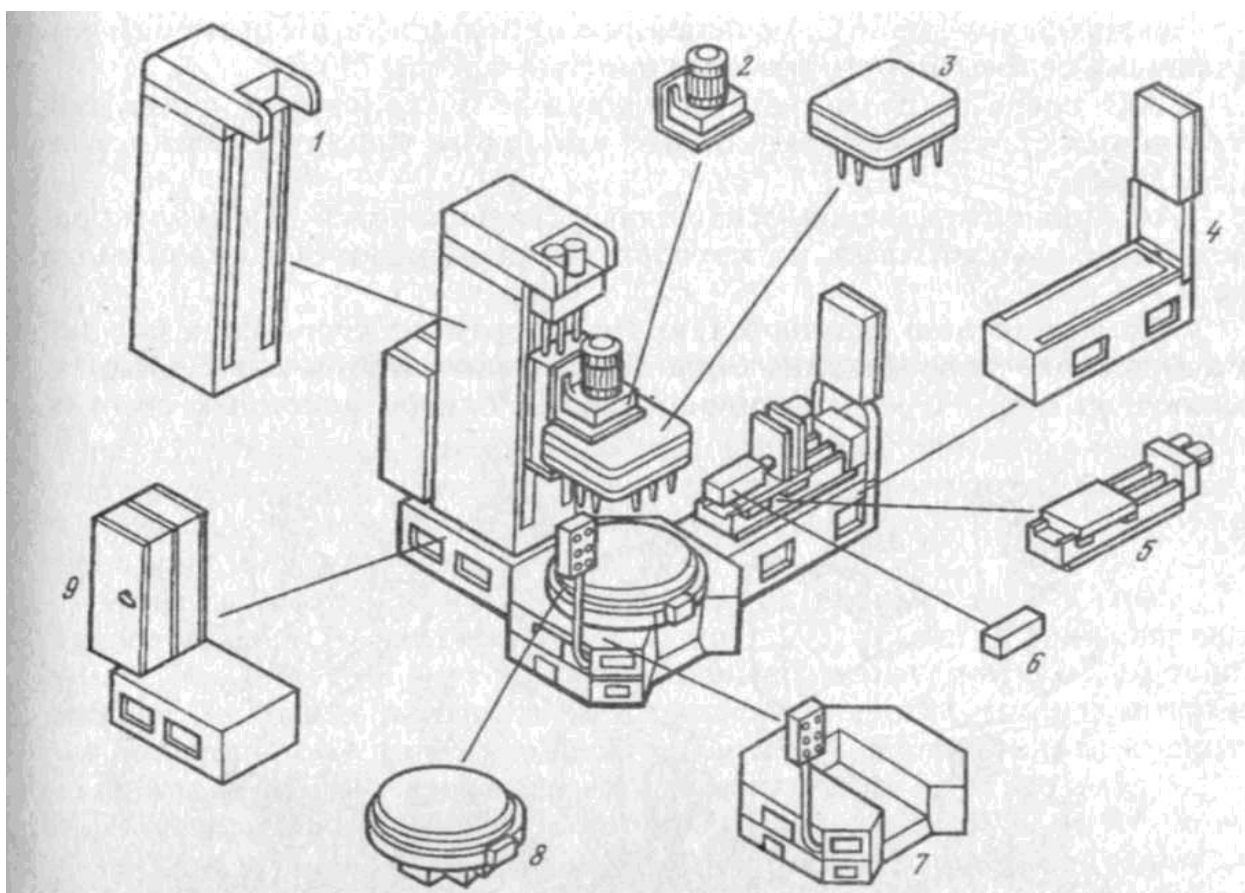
Составные элементы агрегатного станка: 1 – стойка, 2 – силовая бабка, 3 – многошпиндельная коробка, 4 – станина боковая, 5 – силовой стол, 6 – одношпиндельная расточная бабка, 7 – станина центральная, 8 – поворотный делительный стол, 9 – станина-подставка.
